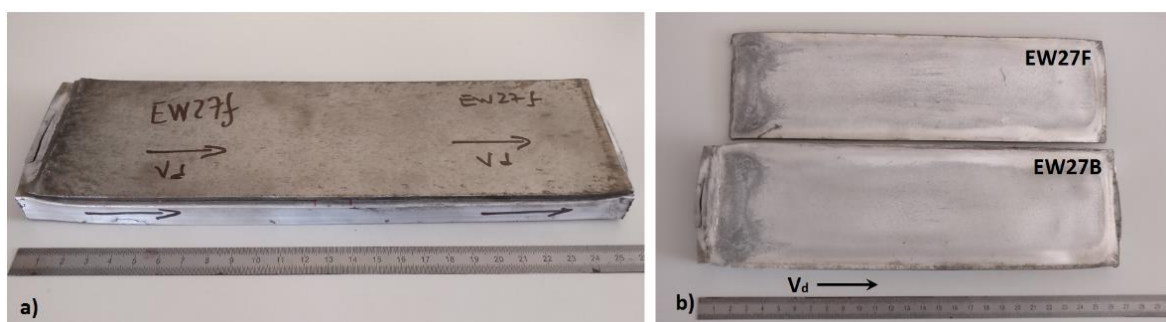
Análise macroscópica da soldadura EW27: a) Peças sobrepostas; b) Peças separadas.
